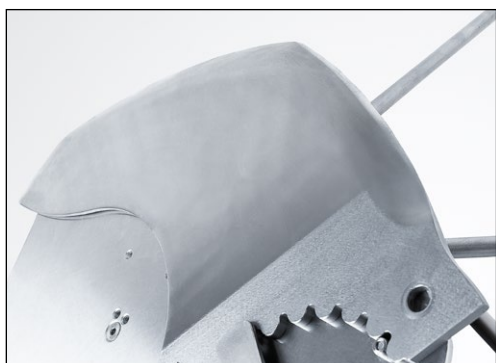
Куттерный нож с предварительной выпуклой заточкой
